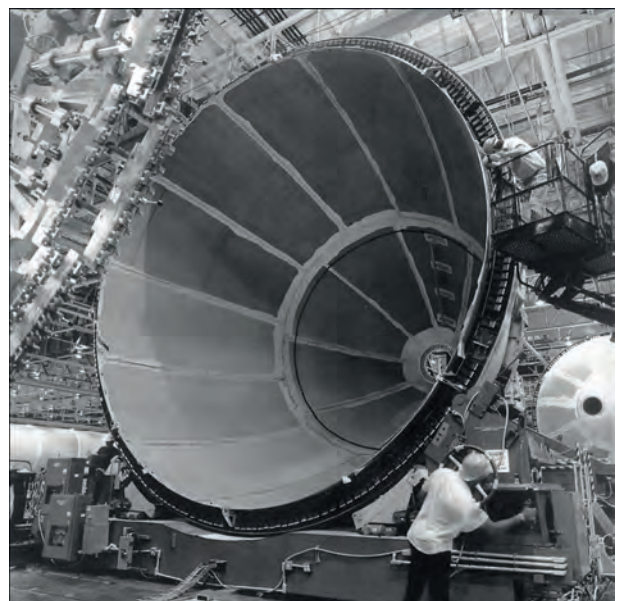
Зварювання купола зовнішнього бака для палива космічного корабля багаторазового використання Space Shuttle (США)
